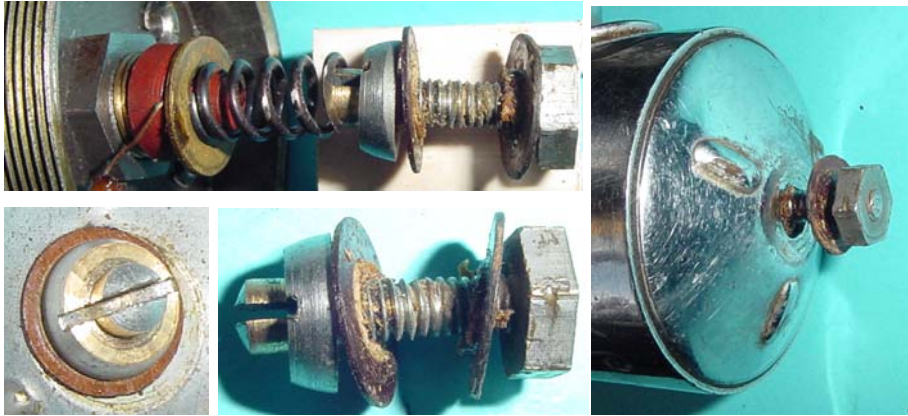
Kontaktteller, Schraubenfeder und Durchführung des Kontaktbolzens durch den Boden
